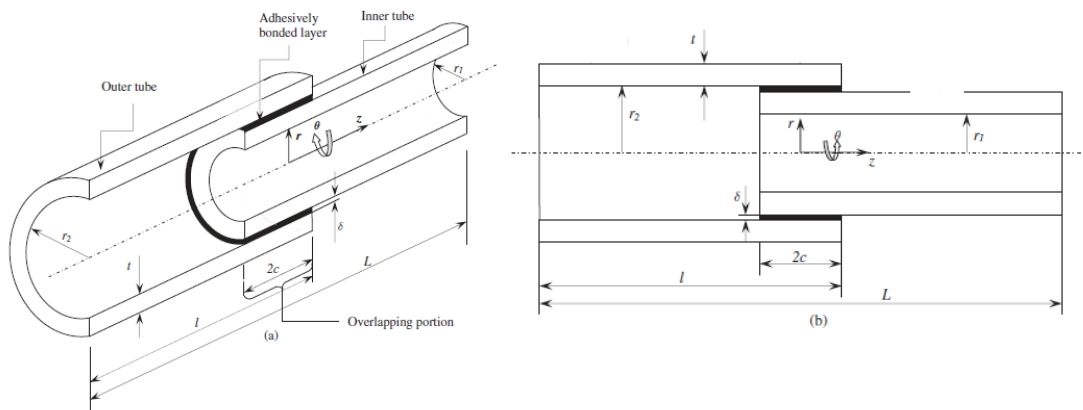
Geometria e configuração da junta tubular colada: (a) Vista isométrica e (b) vista longitudinal [38].
